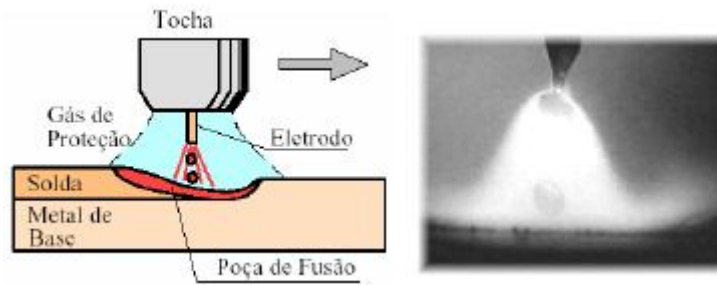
Representação da soldadura MIG/MAG.
